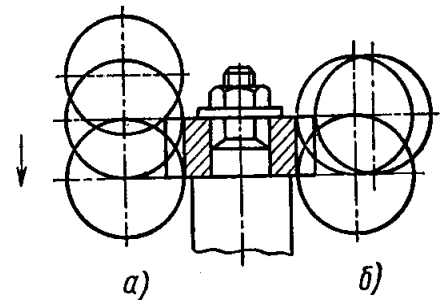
Схеми врізання черв'ячної фрези:
